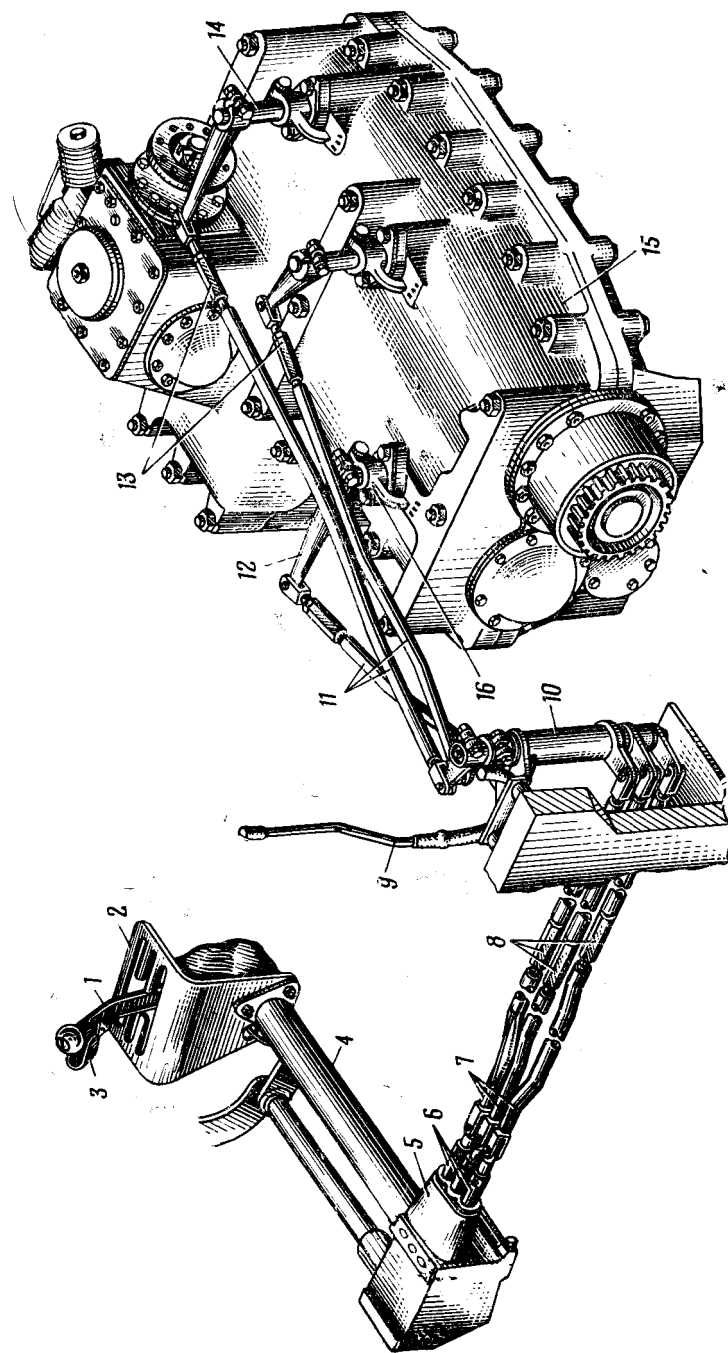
Привод управления коробкой передач: 1 — рычаг кулисы; 2 — козырек кулисы; 3 — рукоятка; 4 — труба; 5 — поводковая коробка; 6 — выемка; 7 — продольные тяги; 8 — стяжные муфты; 9 — трубка; 10 — вертикальный валик; 11 — поперечные тяги; 12 — рычаг валика переключения; 13 — муфта; 14 — валик переключения; 15 — коробка передач; 16 — стрелка-указатель
